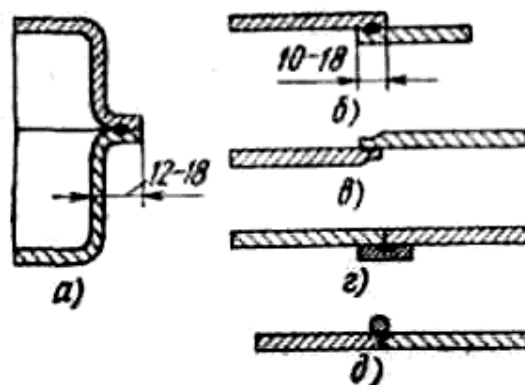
Типы соединений при роликовой сварке: *а* — с отбортовкой; *б* — внахлестку; *в* — с уменьшенной нахлесткой; *г* — с подкладкой; *д* — встык с прутком
